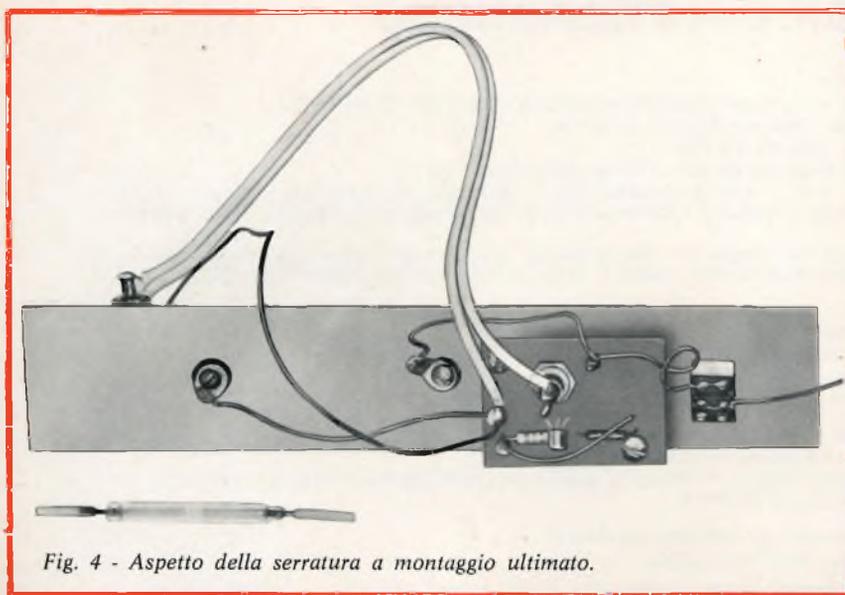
Aspetto della serratura a montaggio ultimato.
